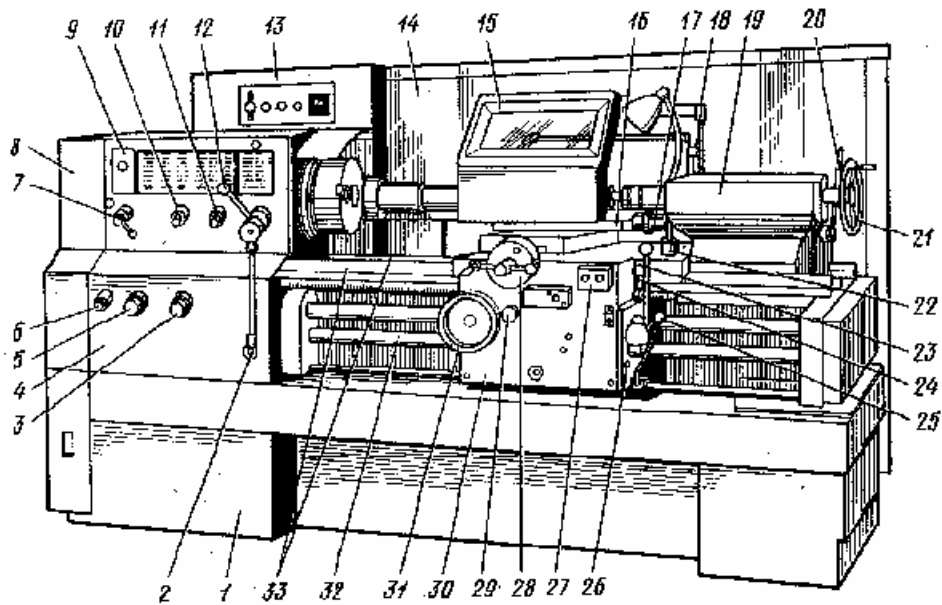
Общий вид и размещение органов управления токарно-винторезного станка мод. 16 K20.
